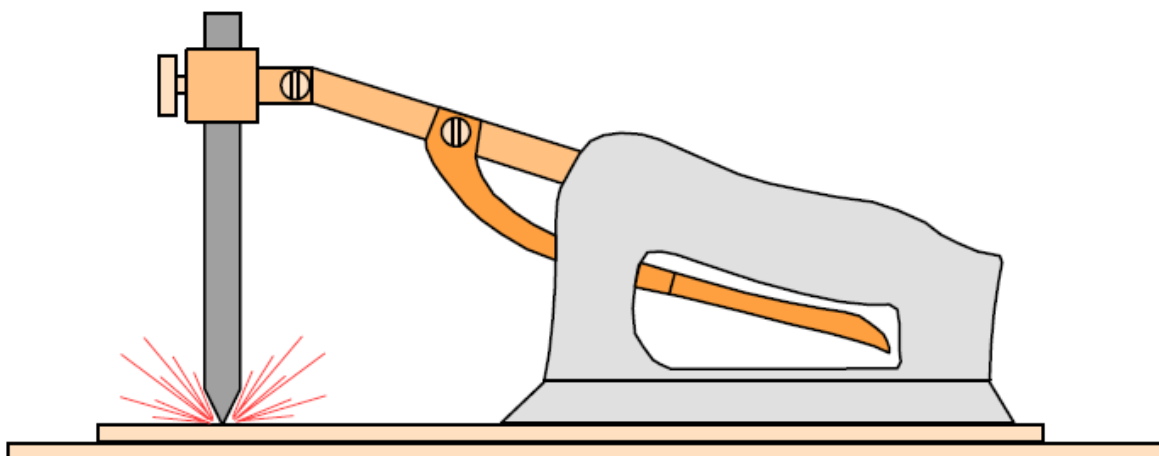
Sistema para soldagem a arco com eletrodo de carvão de Bernados. Fonte: Marques *et al.* (2007)
